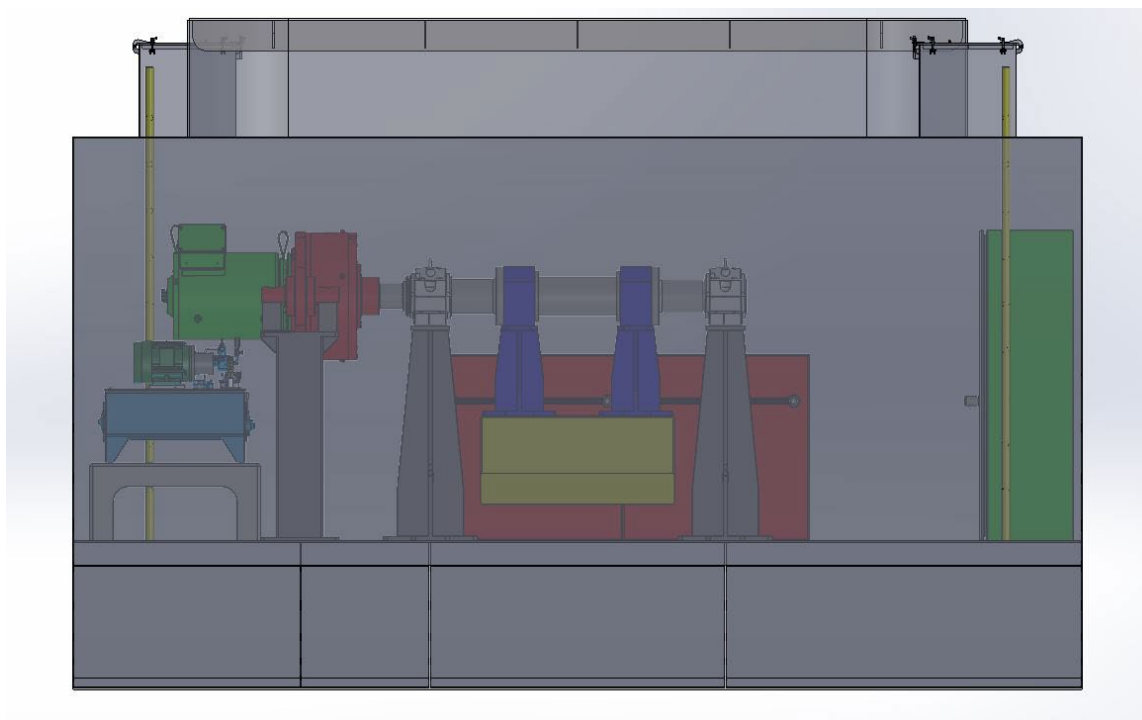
PeWEC – Rappresentazione preliminare del dispositivo, vista laterale
